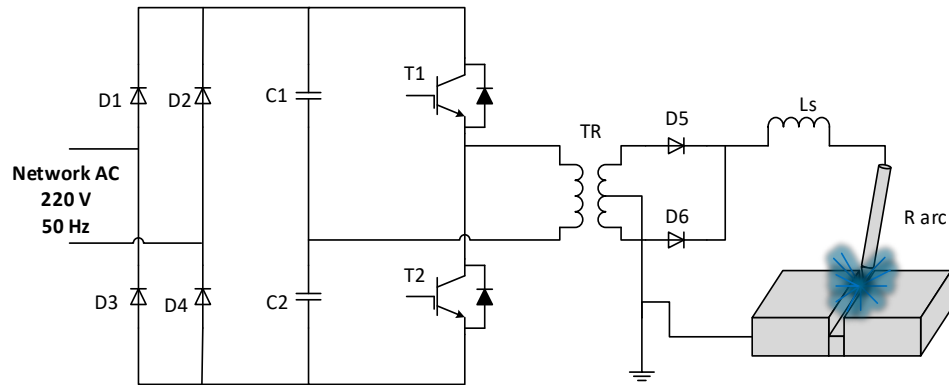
Onduleur de soudage Half-Bridge
